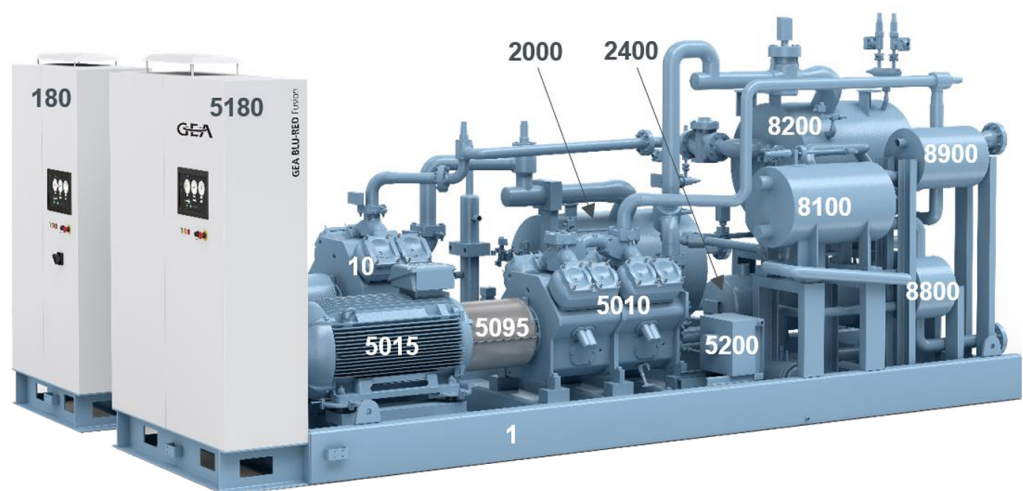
GEA Blu-Red Fusion Ausführungsbeispiel mit Hubkolbenverdichter
